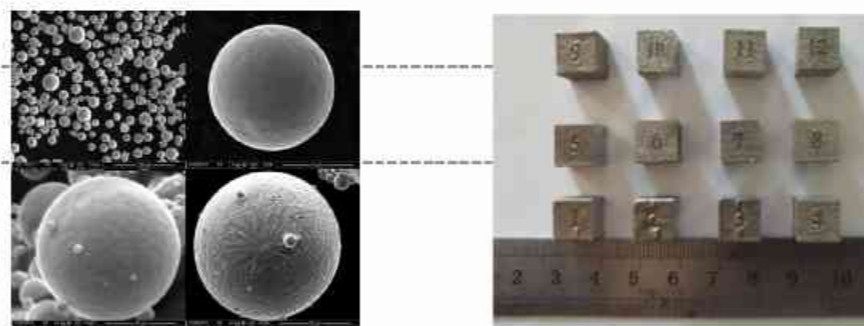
3D 打印用 Inconel 738 合金粉末表面形貌 图 2 不同工艺下选区激光熔化成形 Inconel 738 合金试样
